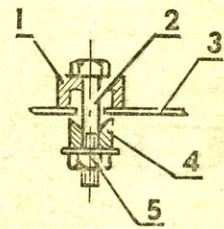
Устройство для просечения круглых отверстий в листовом металле:
